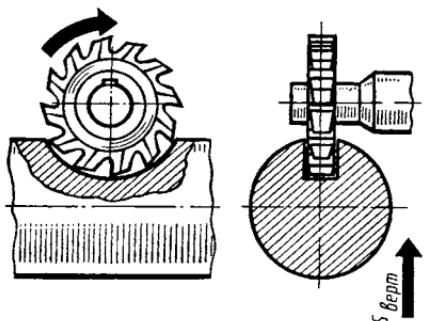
Фрезерование шпоночных пазов под сегментные шпонки.
